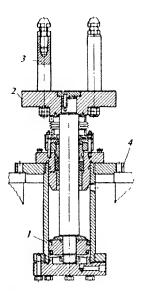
Выталкиватель гидравлический: I – пидроцилиндр; 2 – плита; 3 – штырь; 4 – плита крепления выталкивателя
